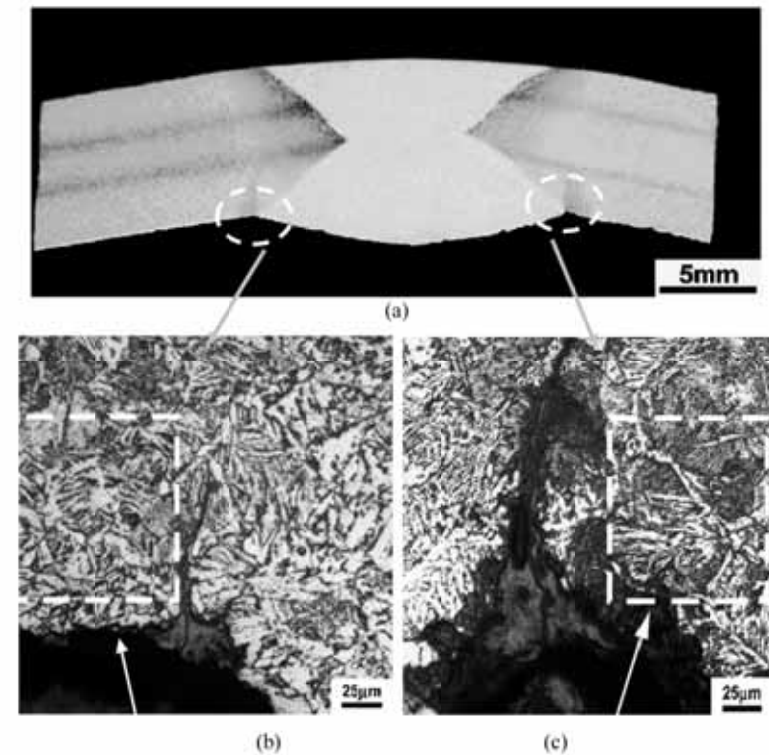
Región alejada de la grieta pasante. Corte transversal: (a) Examen macroscópico; (b) Superficie interna del tubo. Detalle de la microestructura en la región entre la ZAC y el cordón de soldadura, región a la izquierda del cordón de soldadura; (c) Superficie interna del tubo. Detalle de la microestructura en la región entre la ZAC y el cordón de soldadura, región a la derecha del cordón de soldadura. Se observa que dos grietas son formadas en la interface entre la ZAC y el cordón de soldadura, al lado de los defectos de la soldadura. Regiones geométricamente simétricas de la ZAC presentan microestructuras diferentes (áreas rectangulares puntilladas). Ataque: Nital. MO [248].
